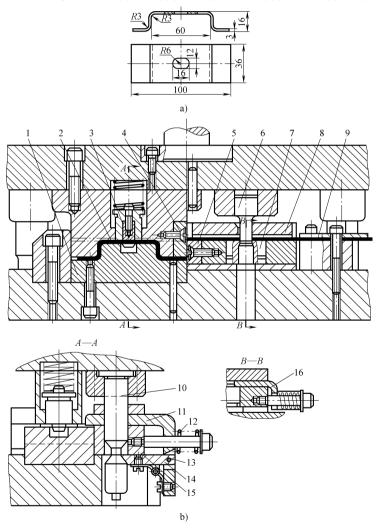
端罩多工位级进模 a) 零件图 b) 模具结构图
